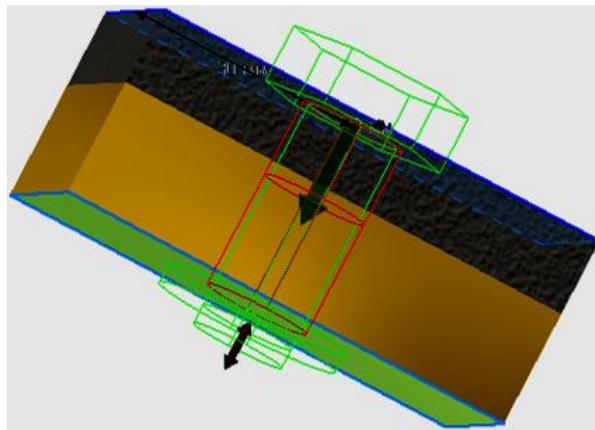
Вид болтового соединения на стадии вставки шайбы
